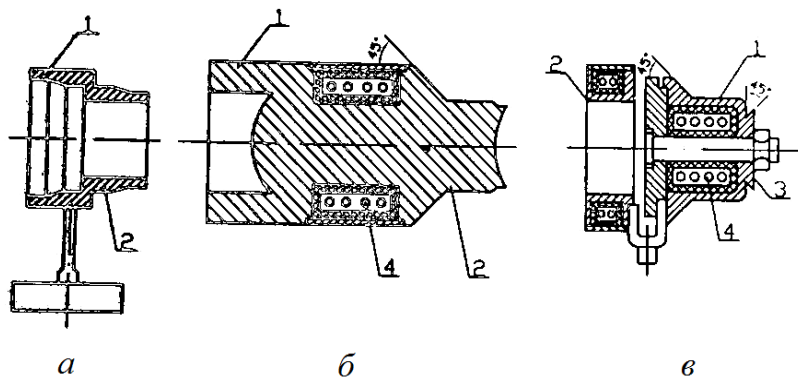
Последовательность процесса сборки и сварки встык:
